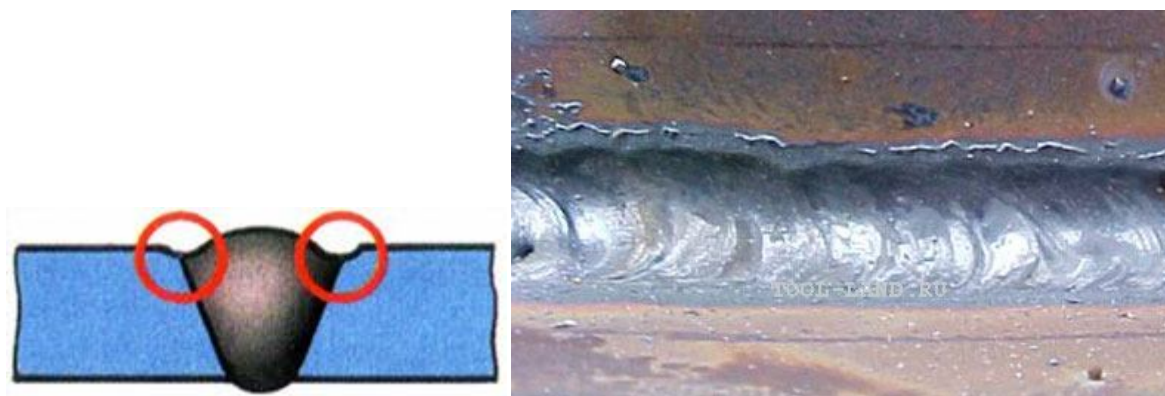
Дефекты сварного шва: подрезы
